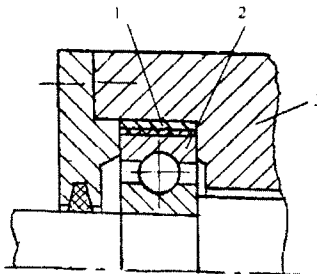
Підшипниковий вузол з гумовометалевим компенсатором
